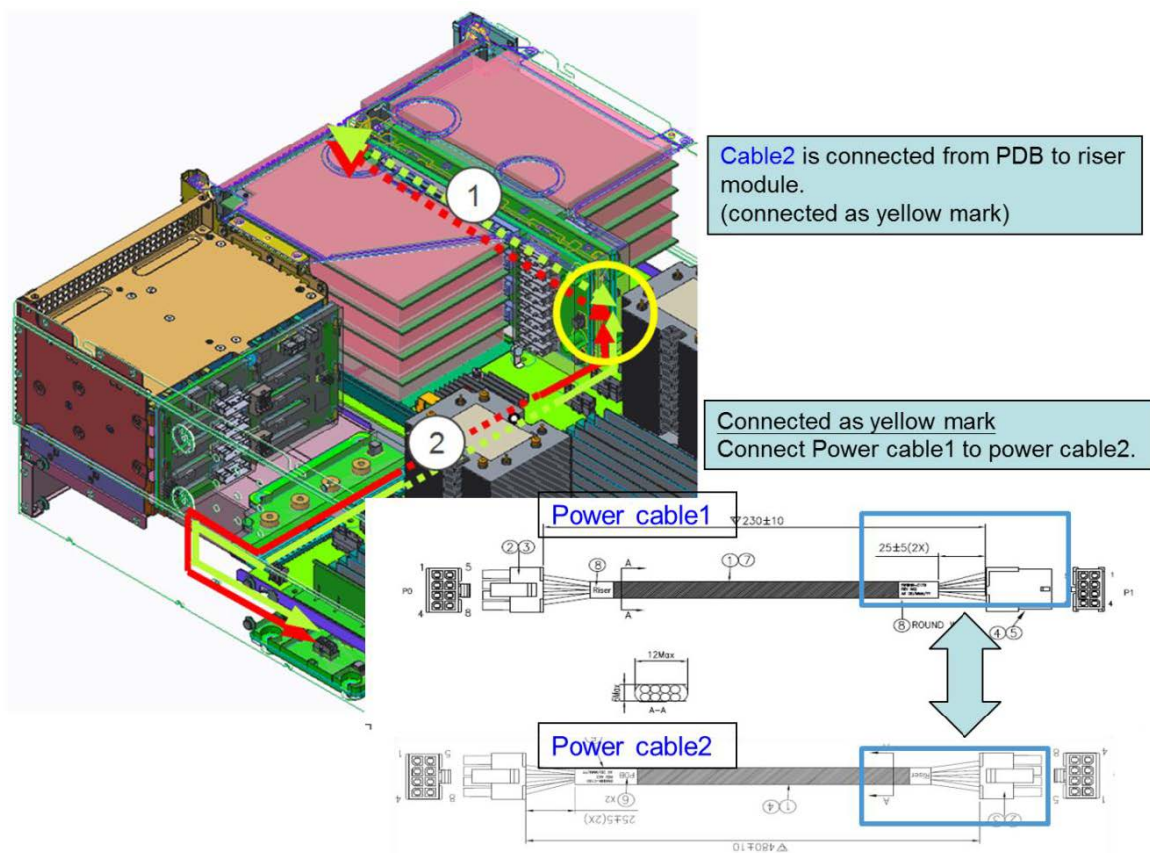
Assemblage du câble d'alimentation 2, carte de montage-PDB, vers carte de montage
